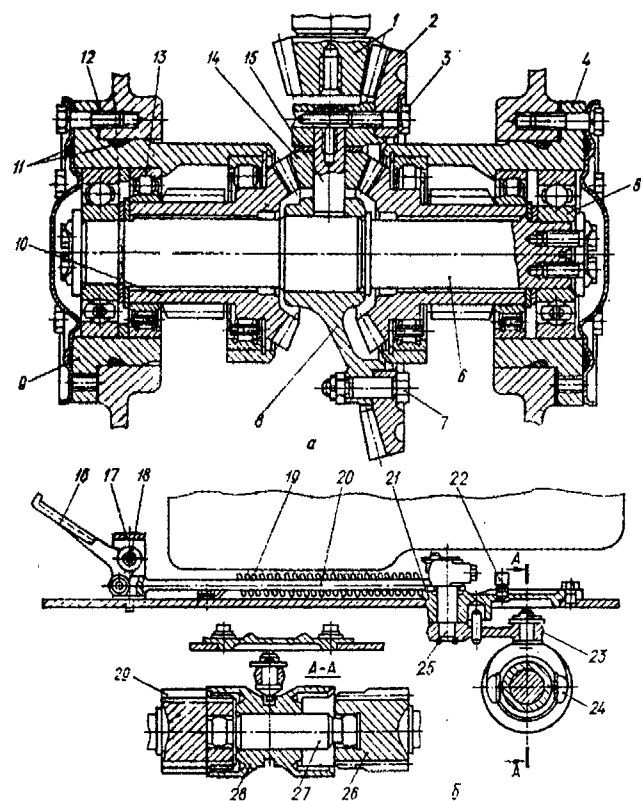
Задний мост тракторов семейства ЮМЗ: 1 – ведущая шестерня; 2 – полуосевая шестерня; 3 – сателлит; 4 – втулка сателлита; 5 – ось сателлита; 6 – специальный болт; 7 – ведомая шестерня; 8 – педаль механизма блокировки дифференциала; 9 – рычаг включения ВОМ; 10 – пружина; 11 – салун; 12 – переводной рычаг блокировки дифференциала; 13 – соединительная муфта; 14 – вал; 15 – шестерня тормозного механизма; 16 – тормоз; 17 – крышка; 18 и 25 – шарикоподшипники; 19 – полуось; 20 – рукав; 21 – ведомая шестерня; 22 – болт; 23 – ВОМ; 24 – муфта включения ВОМ; 26 – роликоподшипник; 27 – прокладка; 28 – стакан подшипника; 29 – вал главной передачи; 30 – ступица
